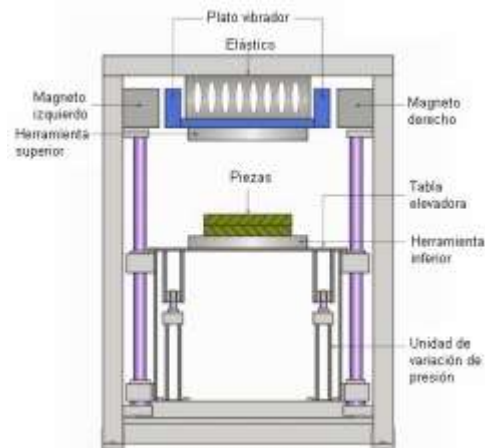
Esquema del equipo utilizado para la soldadura por vibración
